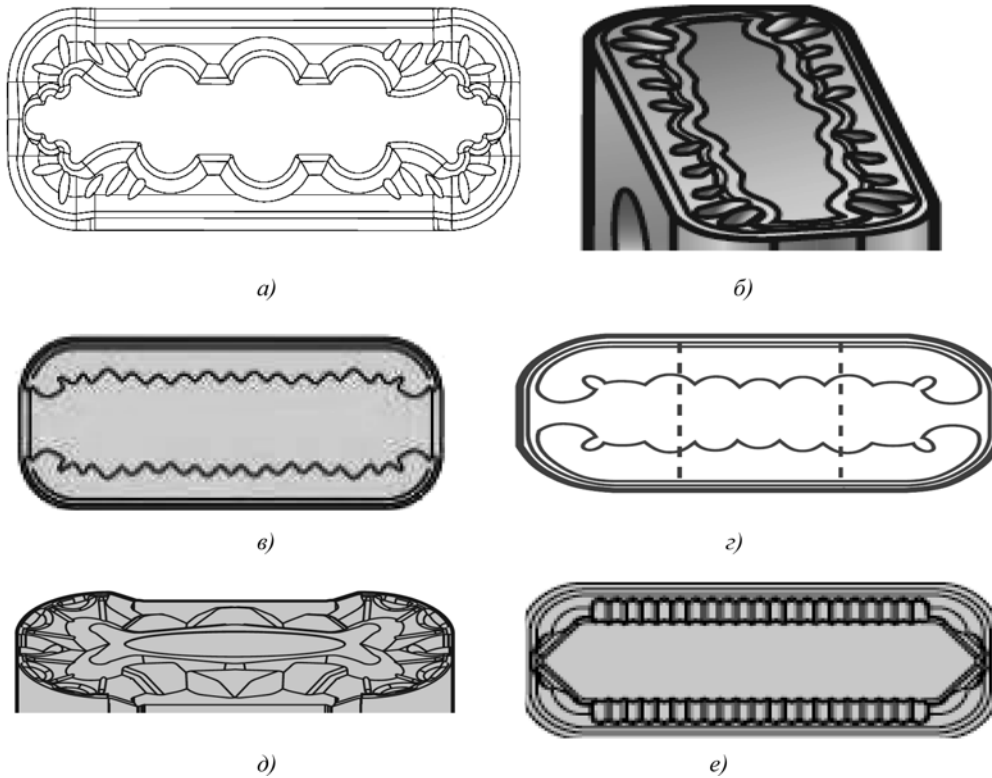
Схемы, отображающие устройство передней поверхности колесотокарных пластин:
